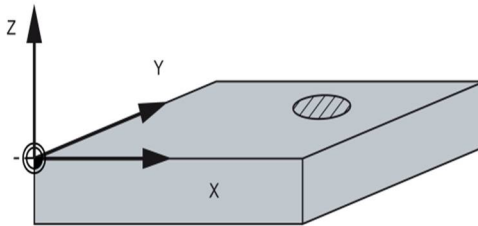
Рекомендована система координат заготовки при фрезерній обробці
